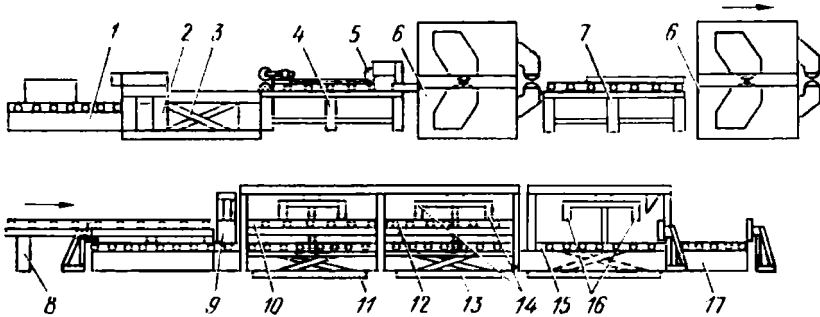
Схема линии калибровки, шлифования и сортировки плит ДЛШ50М:
